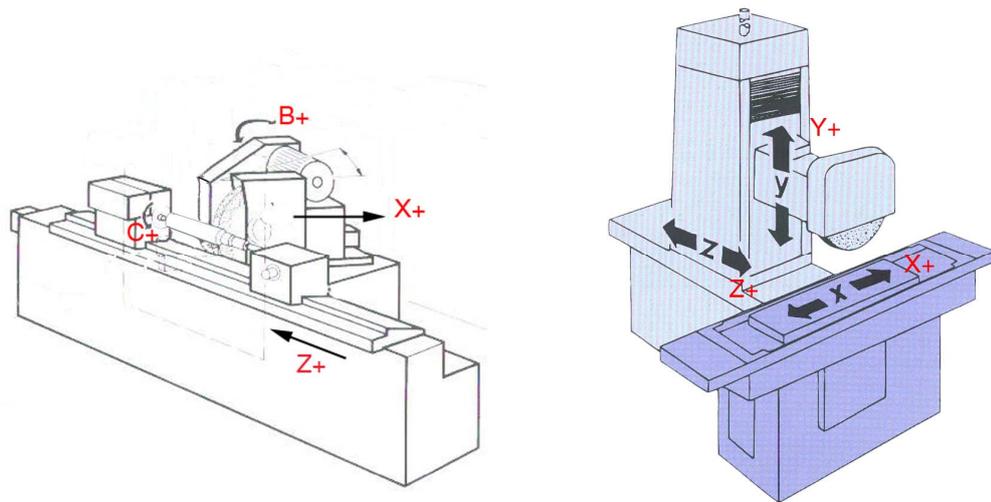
MKS beim Schleifen (Zylinderschleifmaschine, Flachsleifmaschine)
